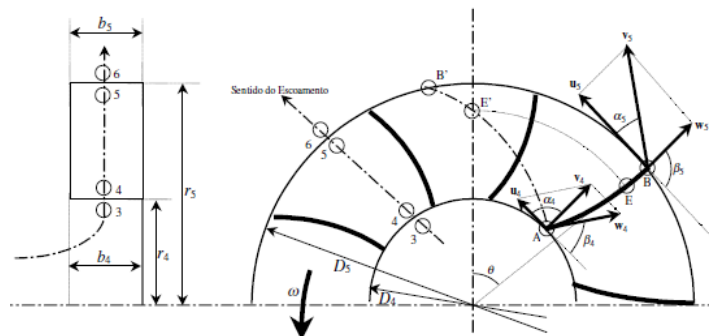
Corte de um rotor segundo um plano perpendicular ao eixo do rotor (Henn, 2001)
